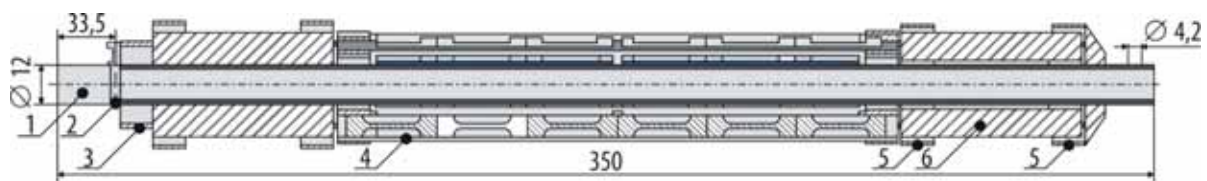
Общий вид подвески с образцами: 1 — держатель; 2 — штифт; 3 — верхние обоймы; 4 — трубка с образцами для испытаний на разрыв; 5 — нижние обоймы; 6 — образец для испытаний на ударную вязкость
